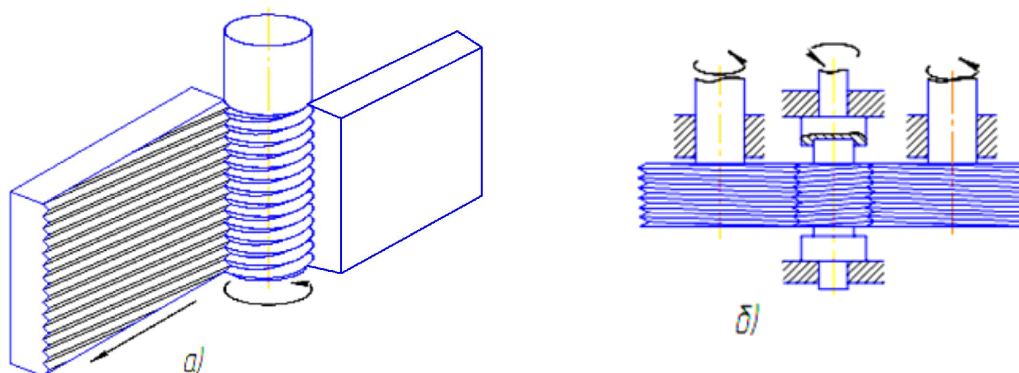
Накатывание резьбы: а — плоскими плашками; б — круглыми плашками (роликами)
